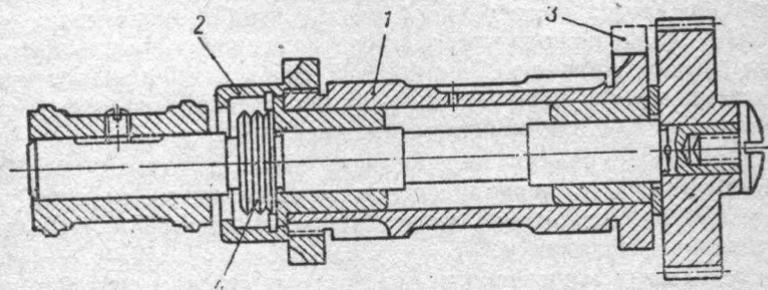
Горизонтальный вал в разрезе: 1 — подшипник; 2 — затяжная гайка; 3 — маслосъемный щиток; 4 — кольцевые виточки
